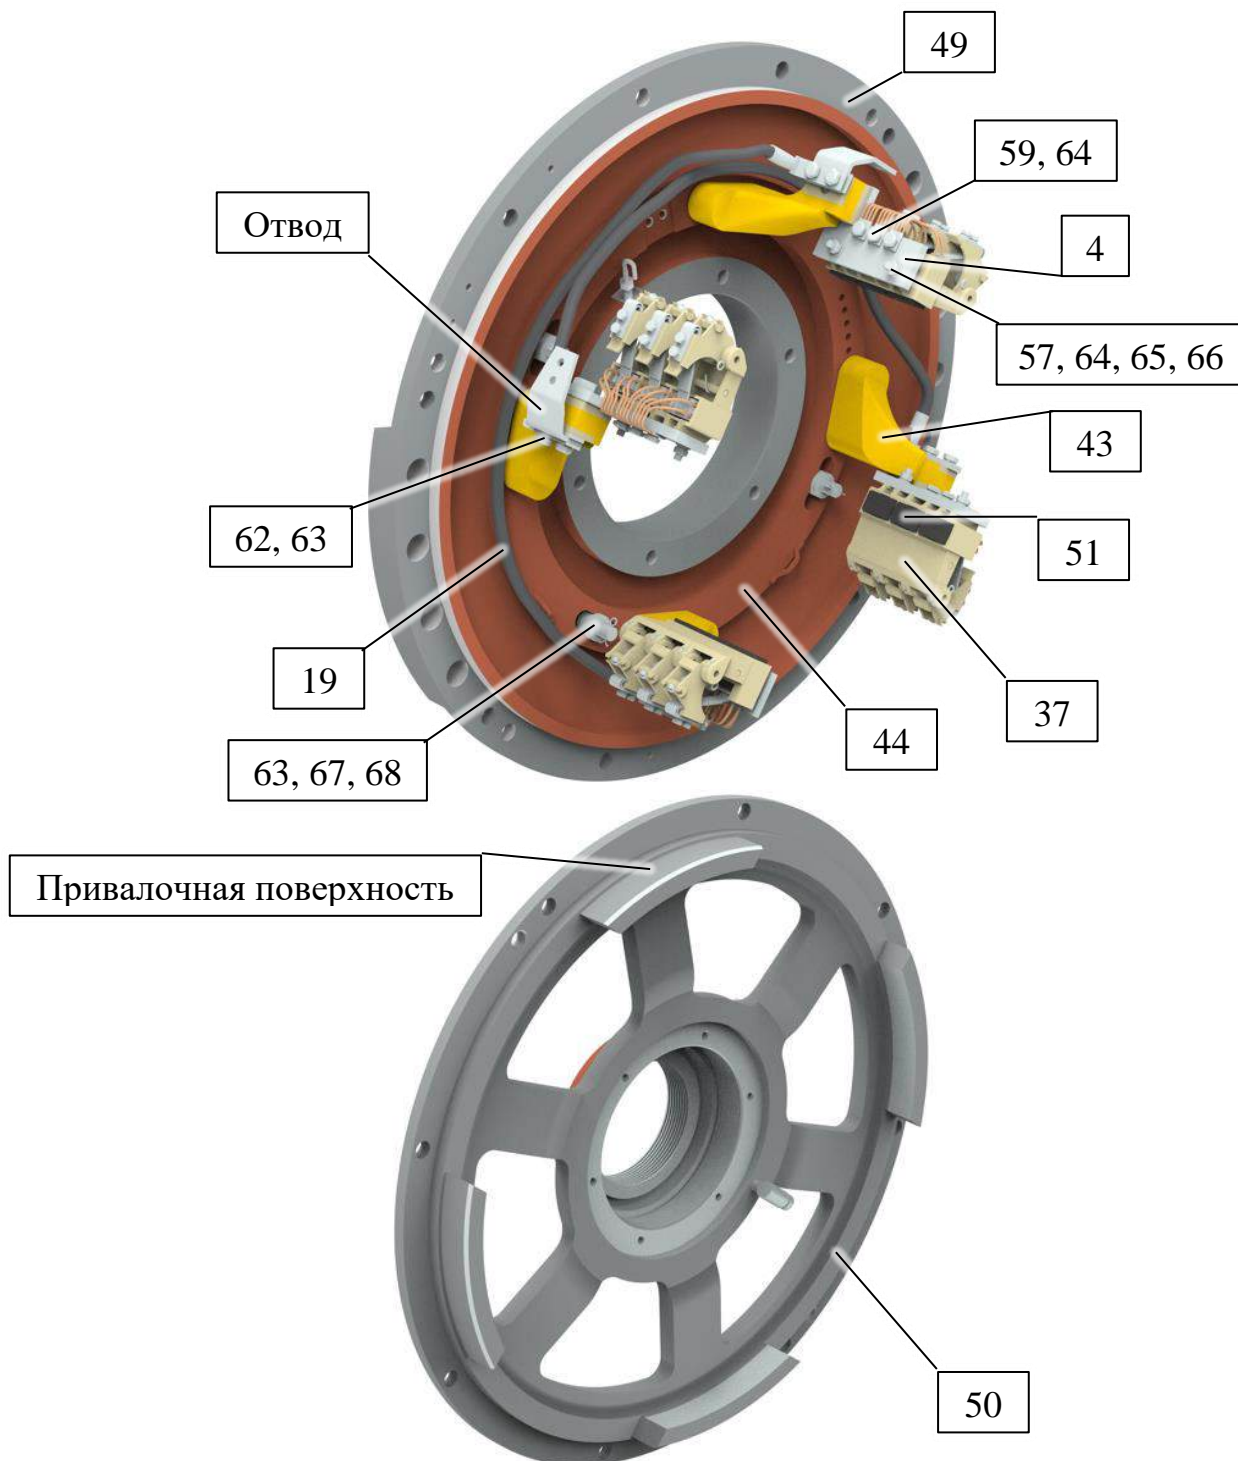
Щиты подшипниковые электродвигателя ЭДП-600, ЭДП-600С
